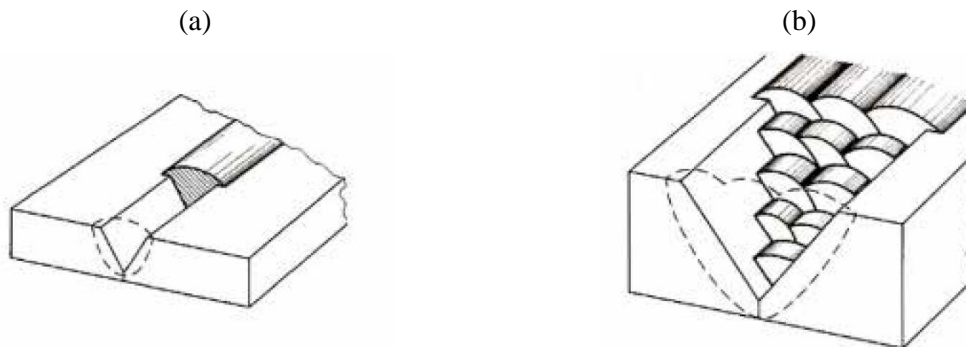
Techniques de soudage monopasse (a) et multipasses (b) (Cazes 2017).
